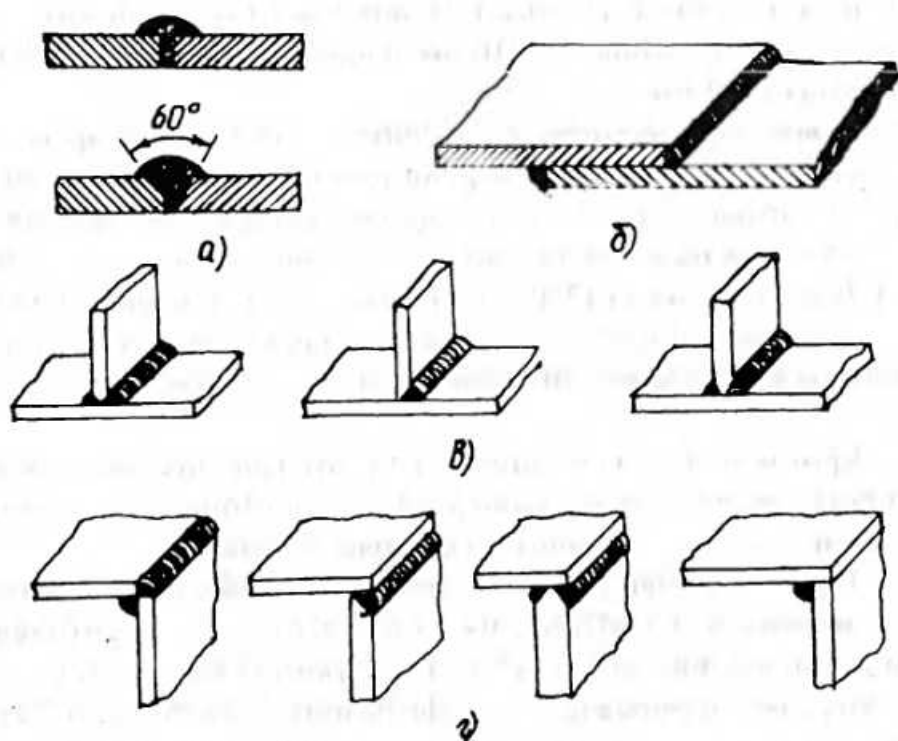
Види зварних з'єднань тонколистового металу: а) стикове (впритул); б) внакладку (внапусток); в) таврове; г) кутове
